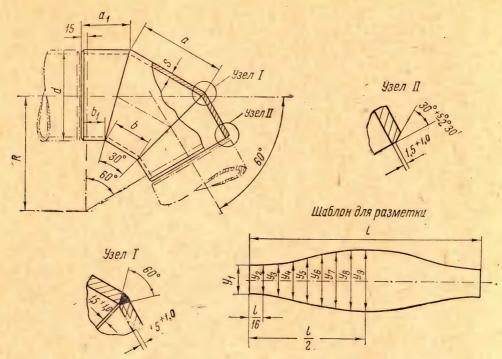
Отвод сварной с углом поворота 60°.
